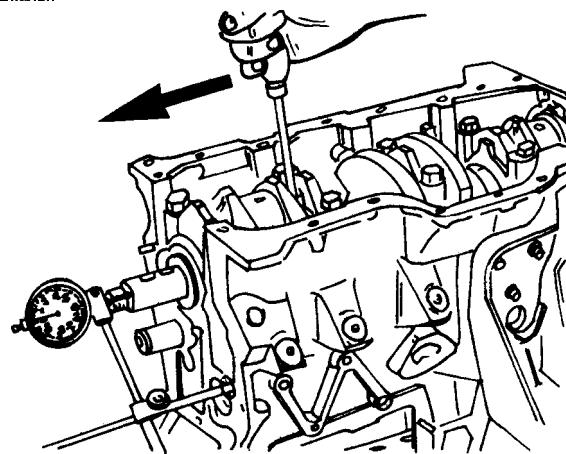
Проверка осевого зазора коленвала с помощью индикатора.
